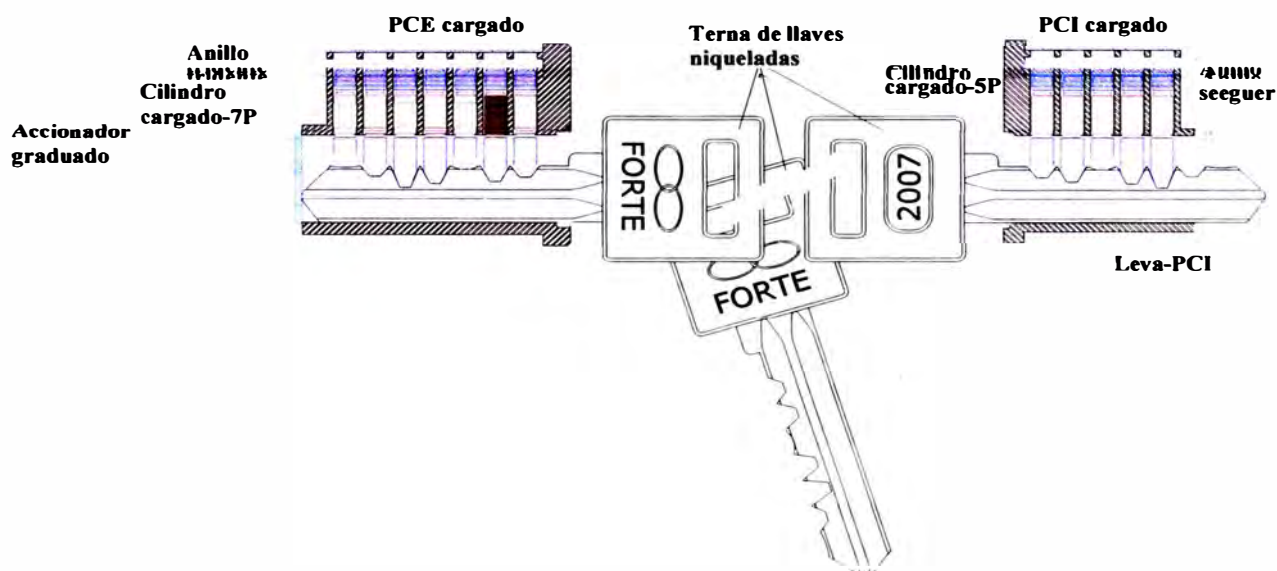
Elementos externos (vista de planta a la izquierda y vista lateral a la derecha)
